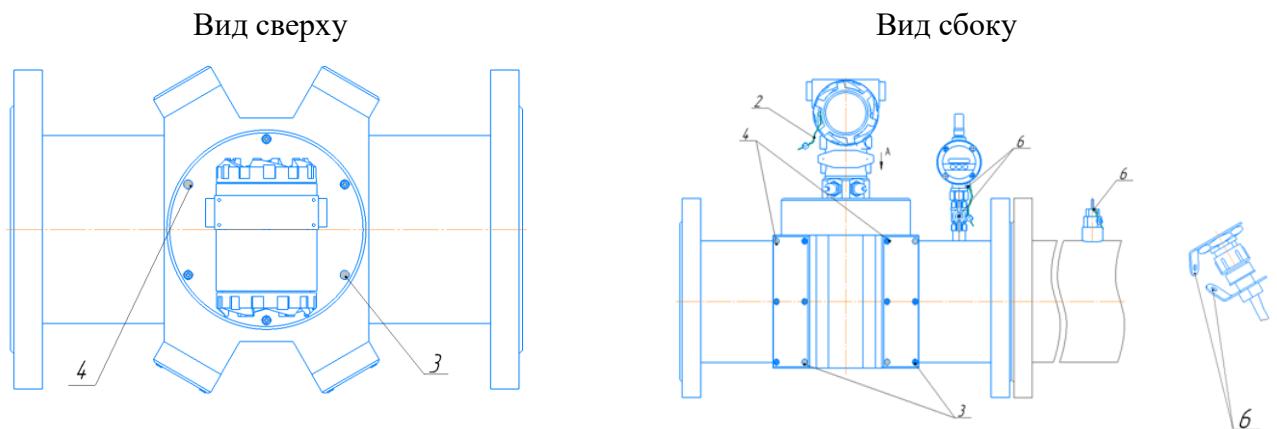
Корпус круглого сечения с раздельными защитными крышками
